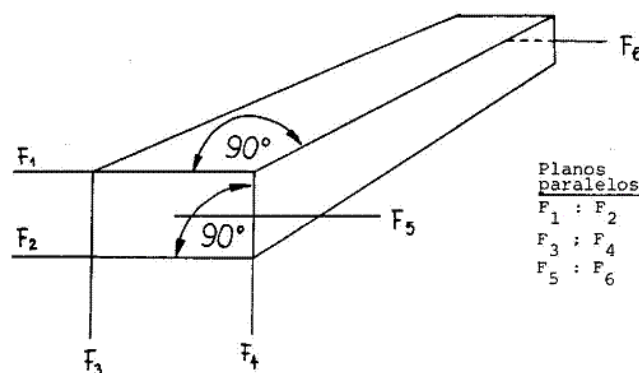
Paralelismo das faces e bordas da madeira serrada.
